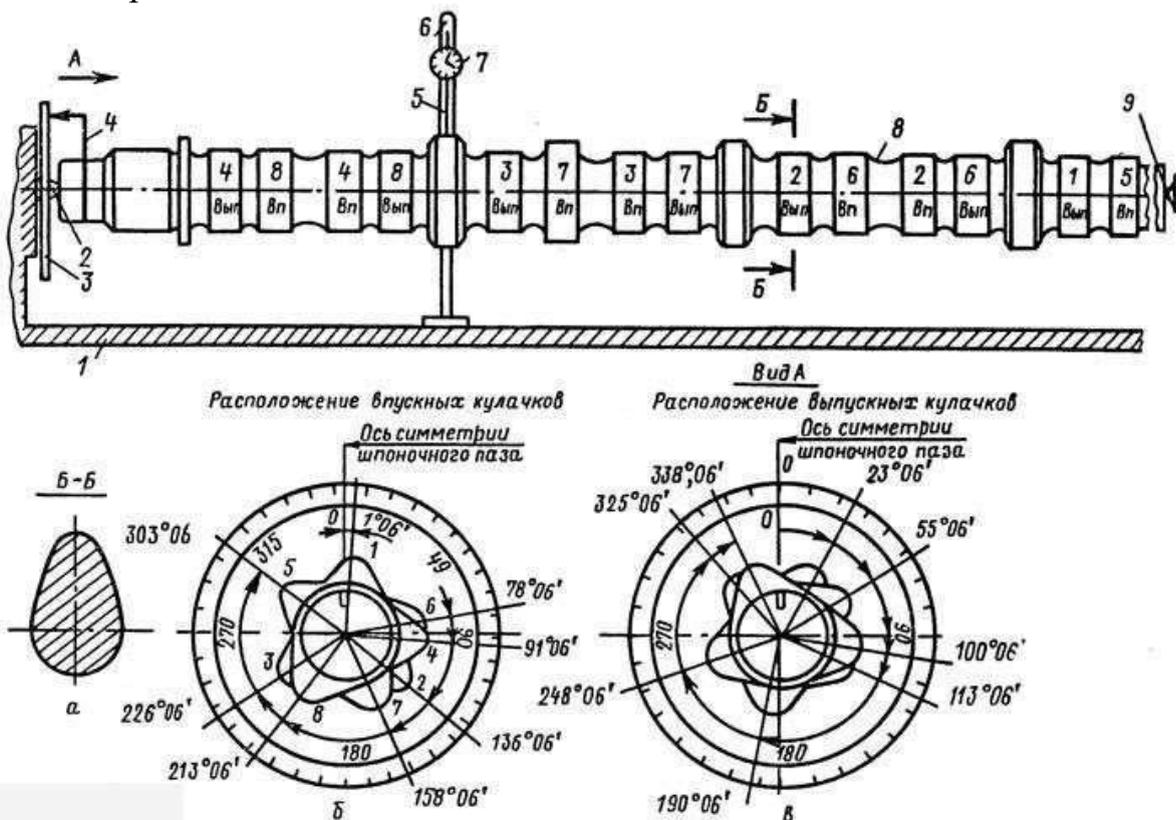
Приспособление для контроля профиля кулачков и опорных шеек распределительного вала
